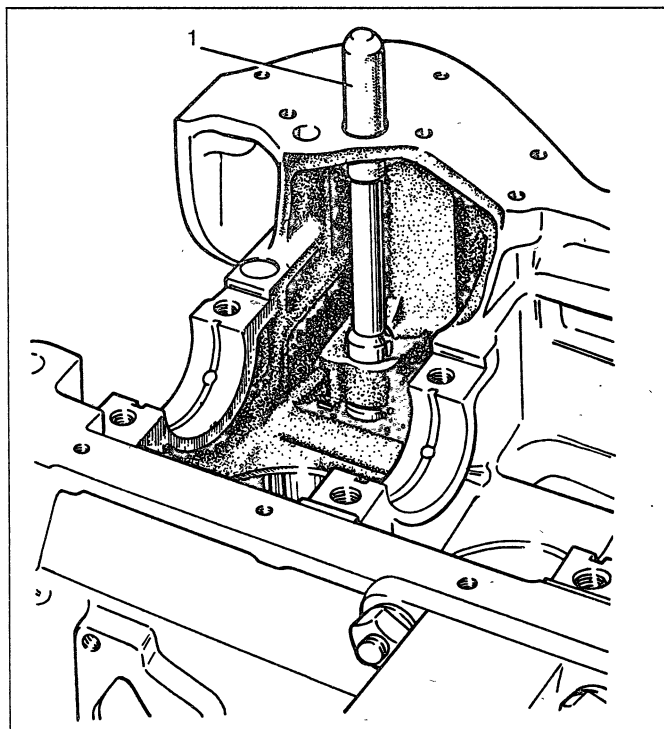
Выпрессовка втулки шестерни привода масляного насоса и распределителя зажигания: 1 – оправка А.60326/R
